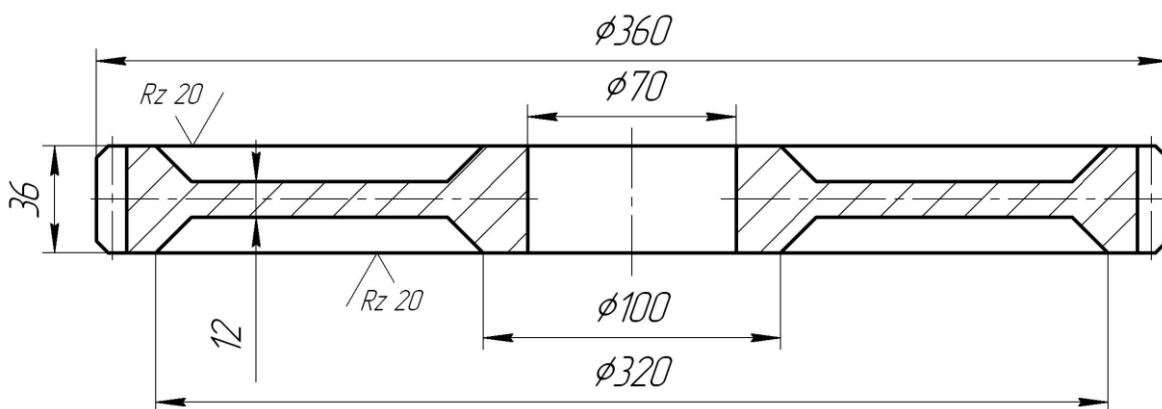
Эскиз детали для определения основных параметров литой заготовки.
